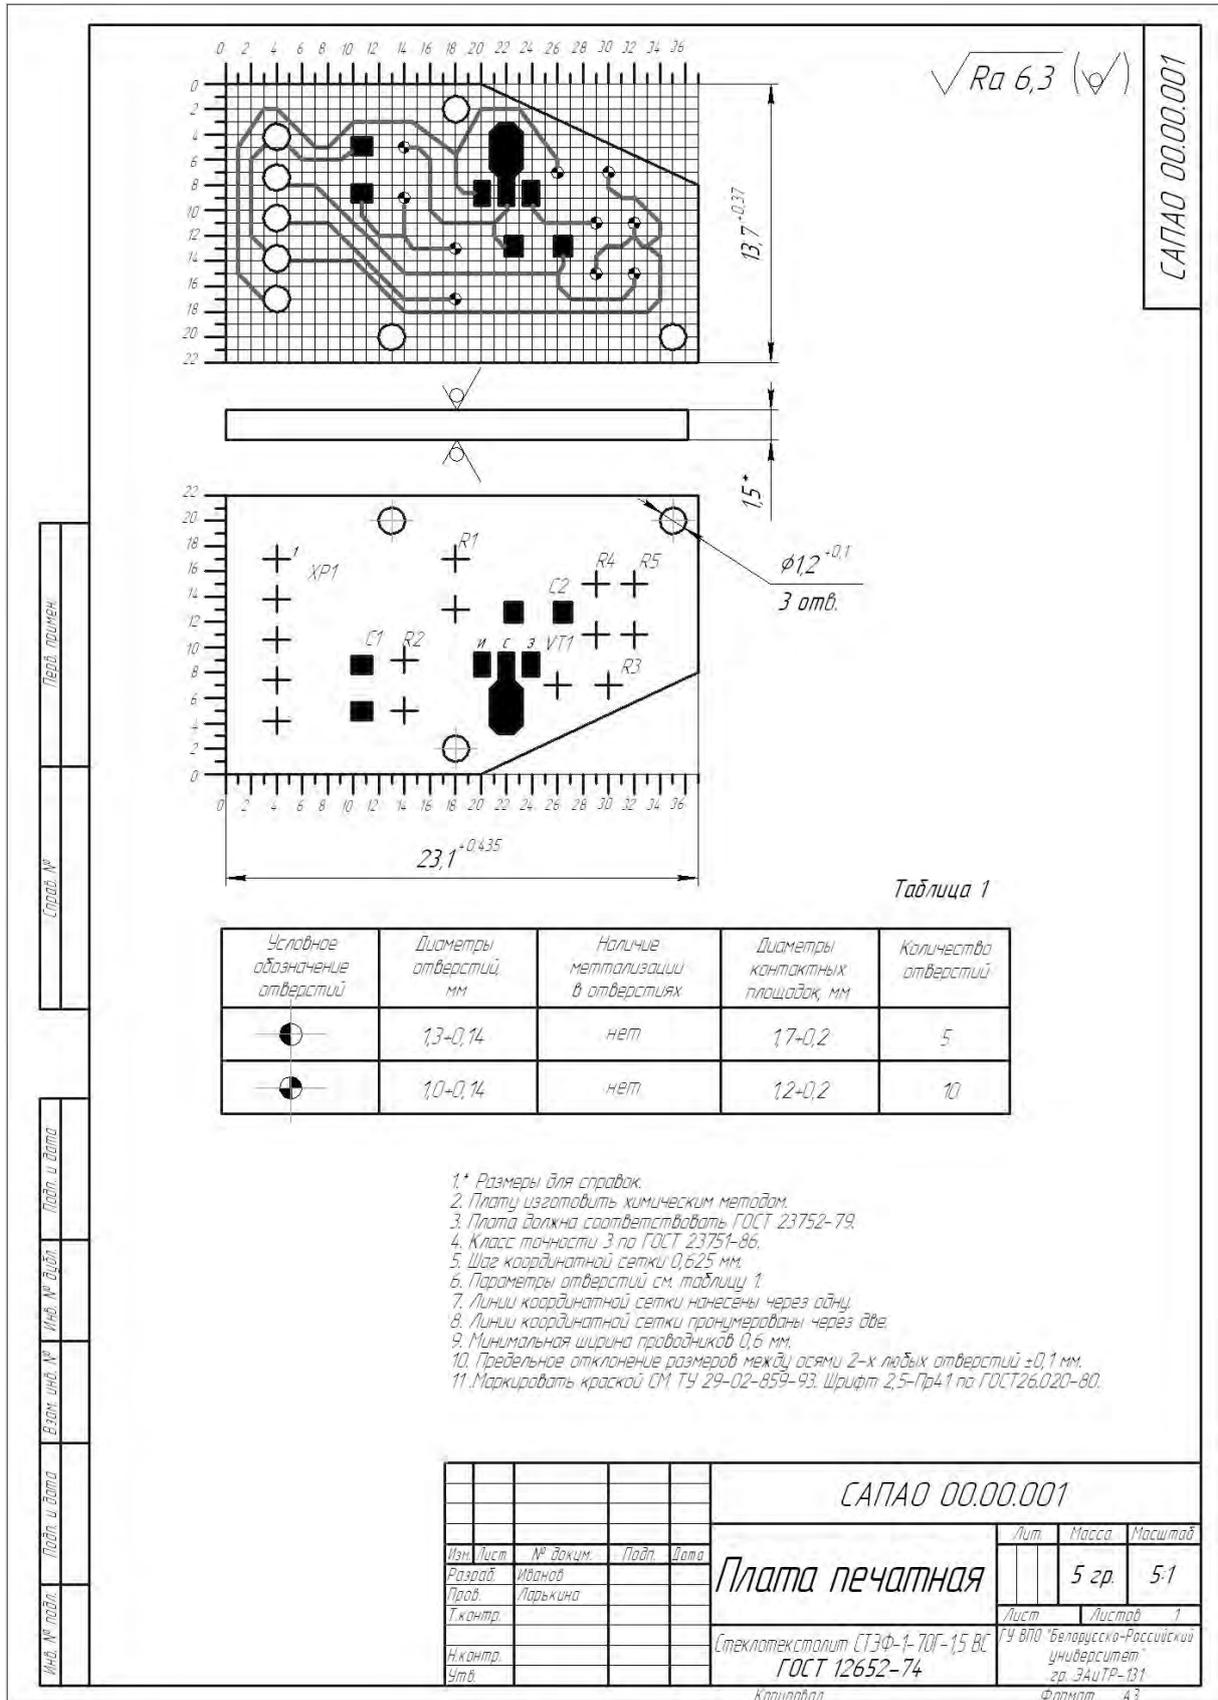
Образец выполнения чертежа платы печатной
